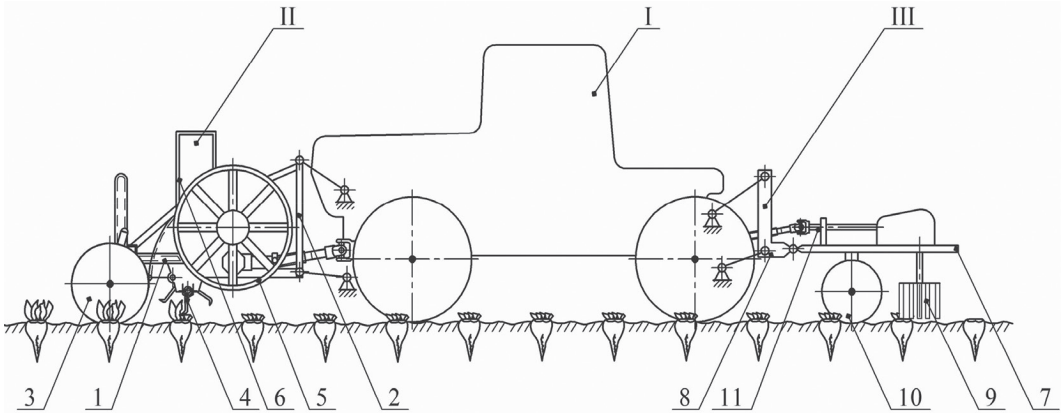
Комбінований агрегат для збирання гички буряку цукрового: I — трактор; II — фронтально навішена гичкозбиральна машина: 1 — рама; 2 — начіпний пристрій; 3 — копіювальне колесо; 4 — роторний гичкорізальний апарат; 5 — транспортно-подавальний робочий орган; 6 — завантажувальний пристрій; III — очисник головок коренеплодів від залишків гички: 7 — рама; 8 — начіпний пристрій; 9 — очищувальний вал; 10 — копіювальне колесо; 11 — привід
